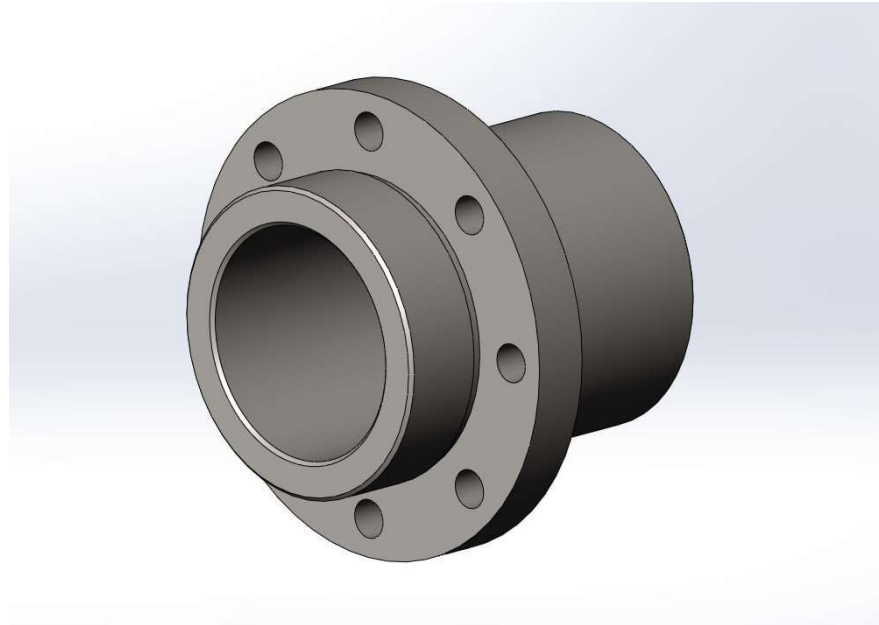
Деталь «Ступиця SK-15.80.50» зображена, як 3D модель
